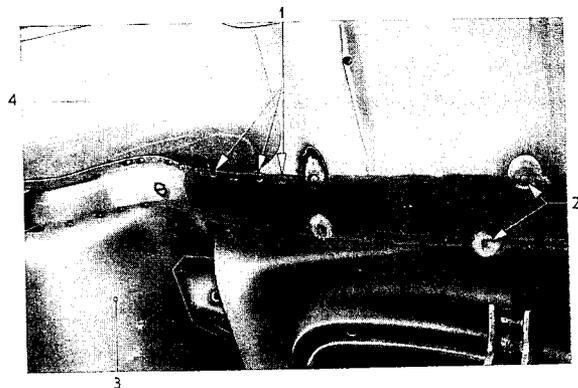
Ausgerissene Schweißpunkte im Bodenblech zuschweißen
